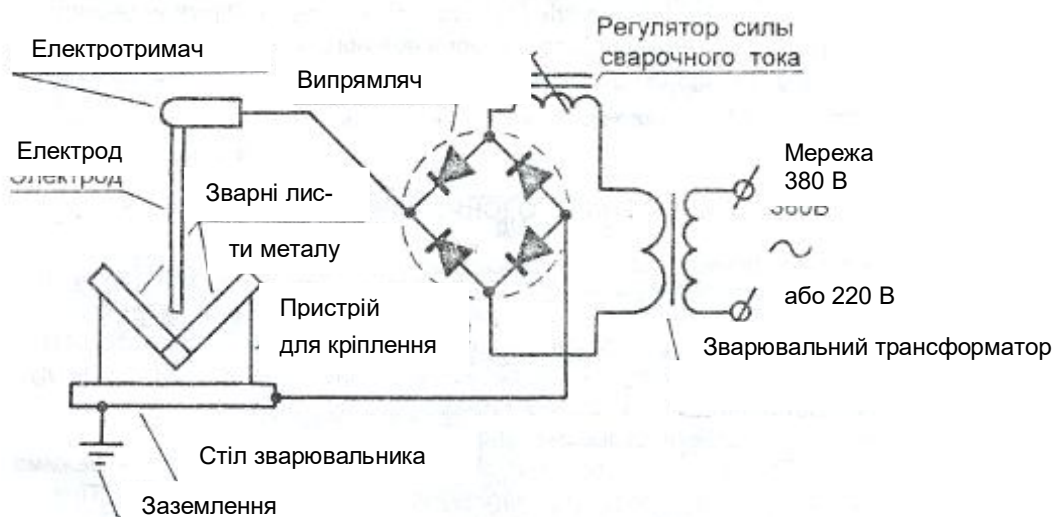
Принципова схема зварювання випрямленим струмом
